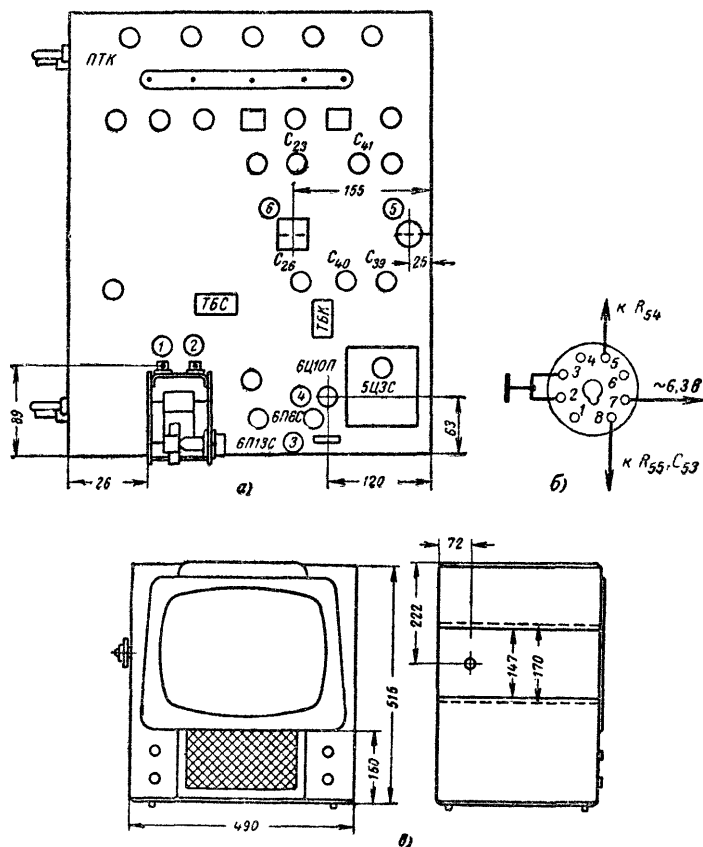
Конструкция телевизора КВН-49-4 с кинескопом 43ЛК2Б.
